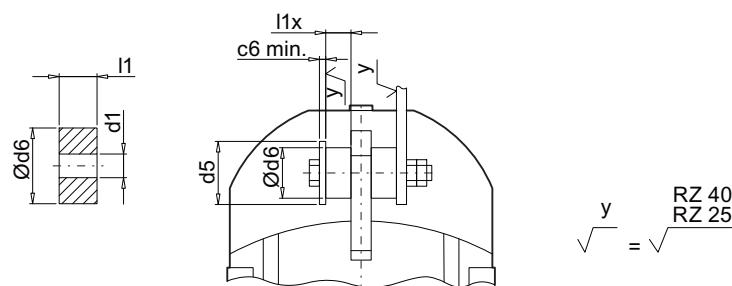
Montagevorschlag für Drehmomentstütze an F.29 - F.149
